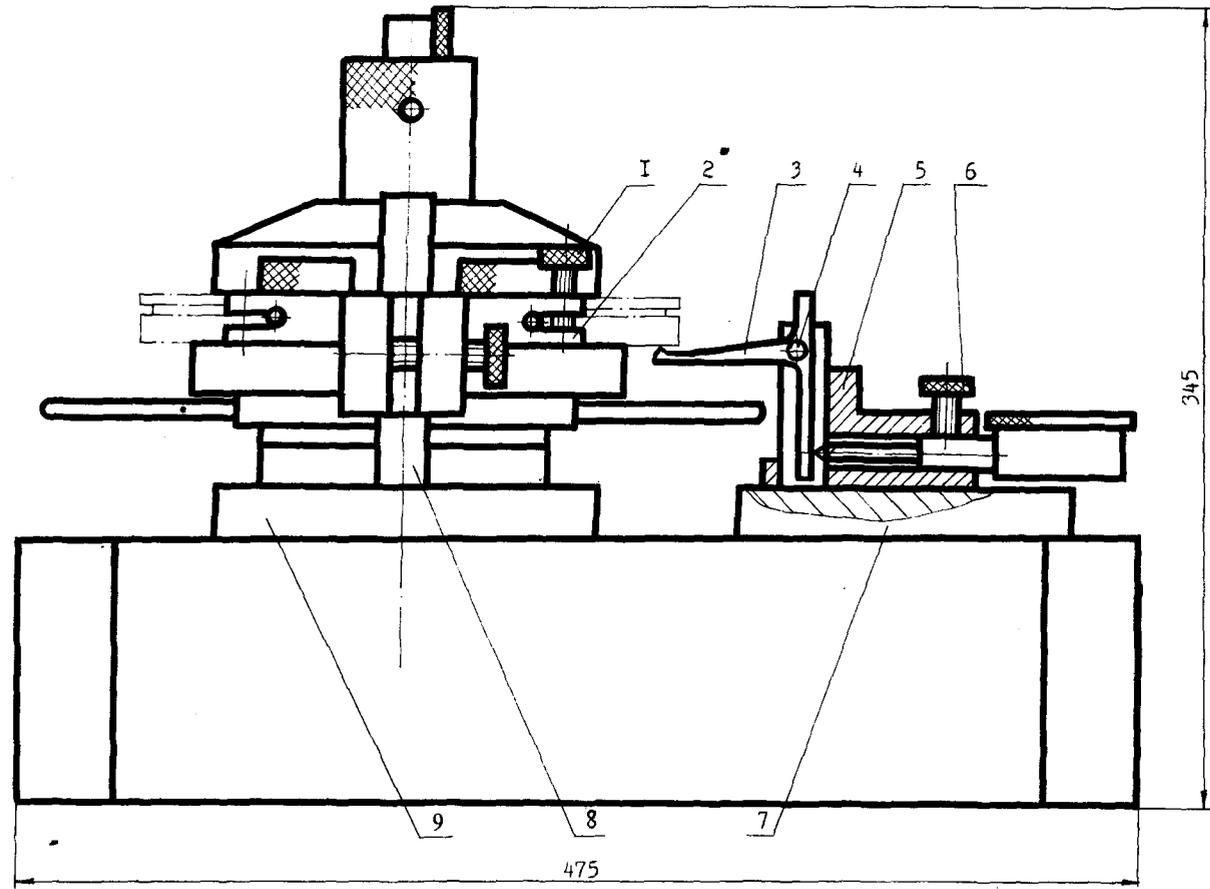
Контрольное приспособление для проверки торцевого и радиального биений (вид Б на рис. 2.2):
